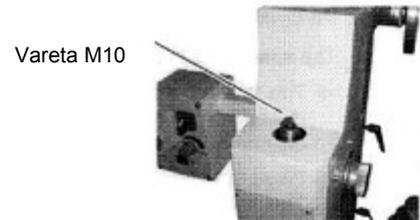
Cabeça de fresagem-furação com a tampa do motor
